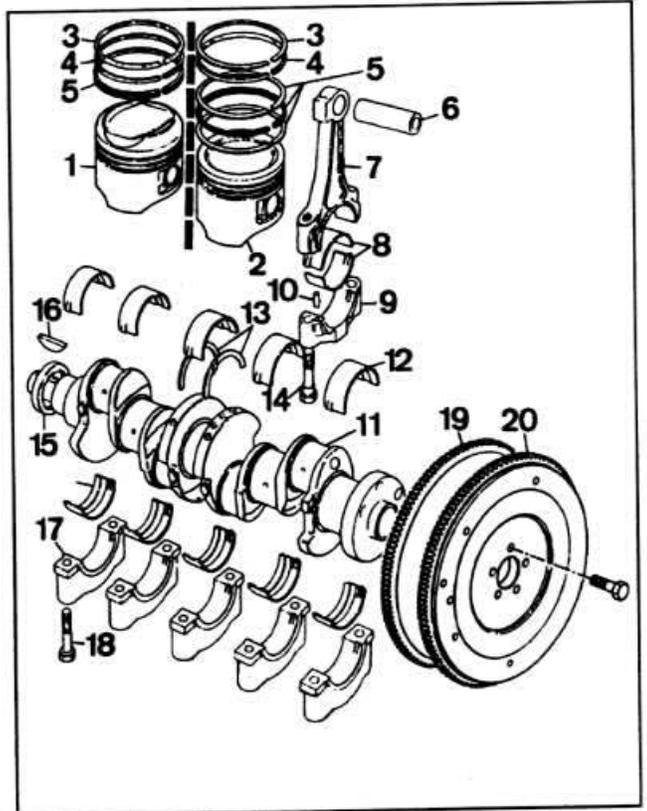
D.59. Кривошипно-шатунный механизм двигателя CVH.
